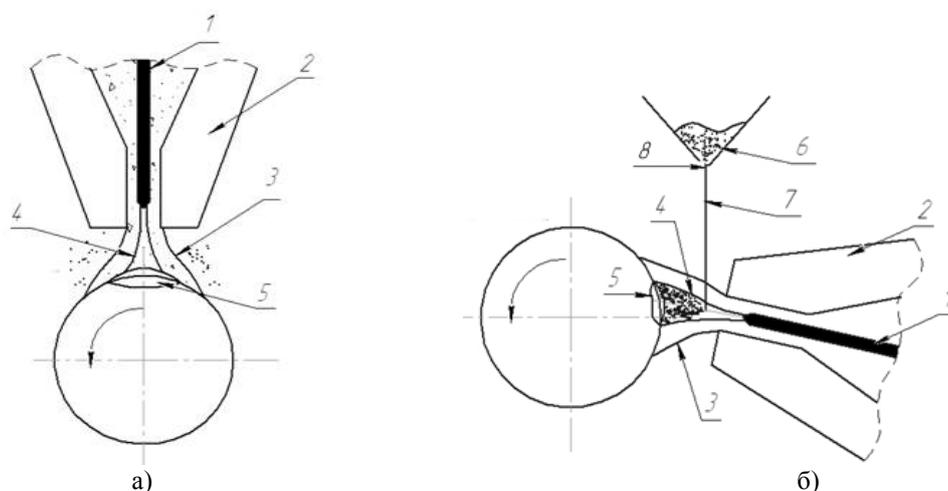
Схемы нанесения износостойких покрытий плазменно-порошковой наплавкой с подачей присадочного материала в плазменную дугу:
